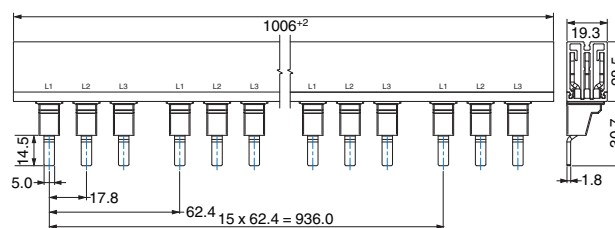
Dimensions de TMC 8...B3...CA (mm)
